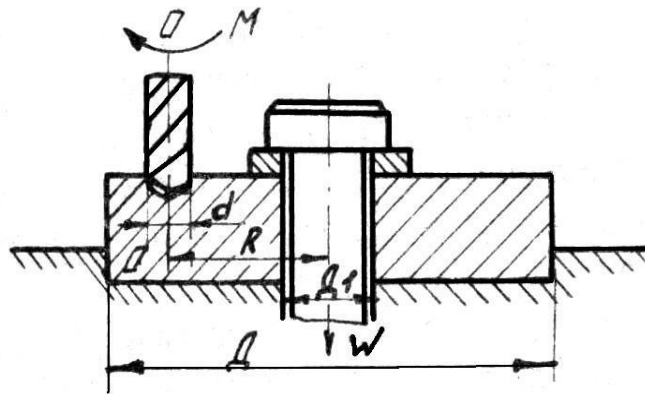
Схема розрахунку затискних зусиль при обробці заготовок на свердлильних верстатах
